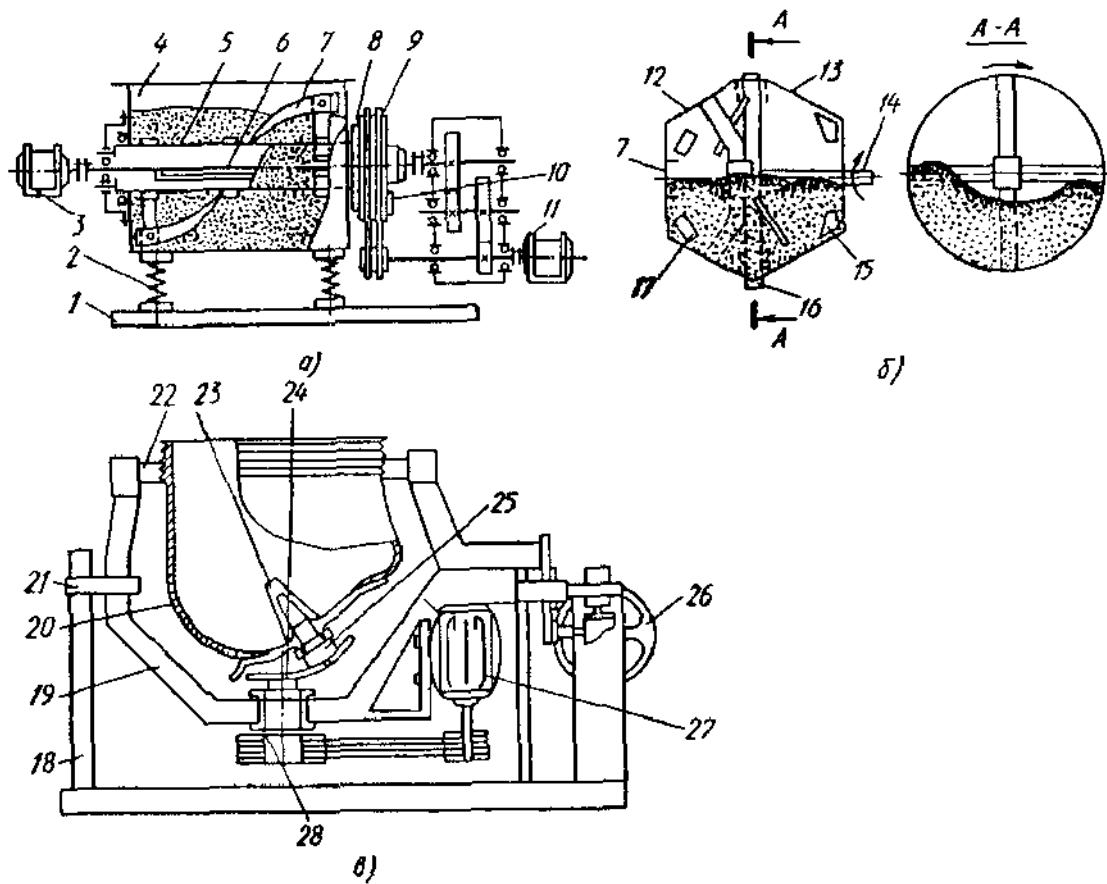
Схемы смесителей интенсифицирующего действия: *а* - двухвальный роторный вибросмеситель; *б* - комбинированный смеситель; *в* - смеситель с гибким корпусом; 1 - рама; 2 - опорные пружины; 3 - электродвигатель привода дебалансного вала; 4 - барабан; 5 - трубчатый вал; 6 - дебалансный вал; 7 - лопасть; 8 - стакан; 9 - приводной шкив; 10 - дебаланс; 11 - электродвигатель привода лопастного вала; 12, 13 - полусферы; 14 - приводной вал; 15, 17 - смесительные лопасти; 16 - резиновое уплотнение; 18 - неподвижная рама; 19 - подвижная рама; 20 - гибкий корпус смесителя; 21 - ось поворота; 23 - опора корпуса; 24 - центральный конус; 25 - кривошип; 26 - механизм опрокидывания; 27 - приводной вал с электродвигателем; 28 - опорный подшипник
